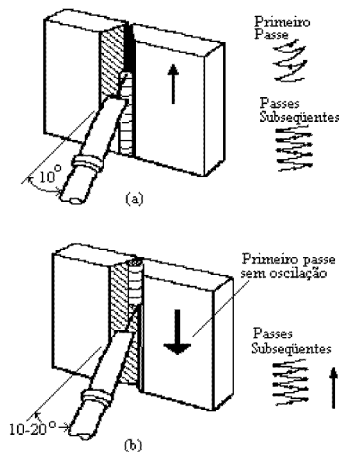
Soldagem de Juntas a Topo: (a) “V” com nariz; (b) “V” simples.
